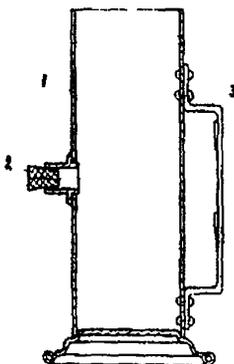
Цилиндр ЦС-2: 1 - цилиндр;
